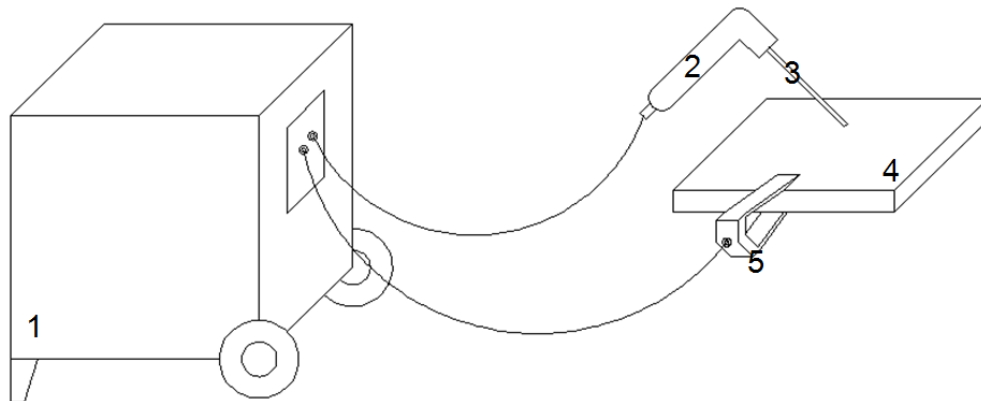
Soldadura por arco: 1. Máquina da soldadura por arco; 2. Porta-eléctros; 3. Eléctrodo; 4. Objecto a soldar; 5. Linha de terra.
